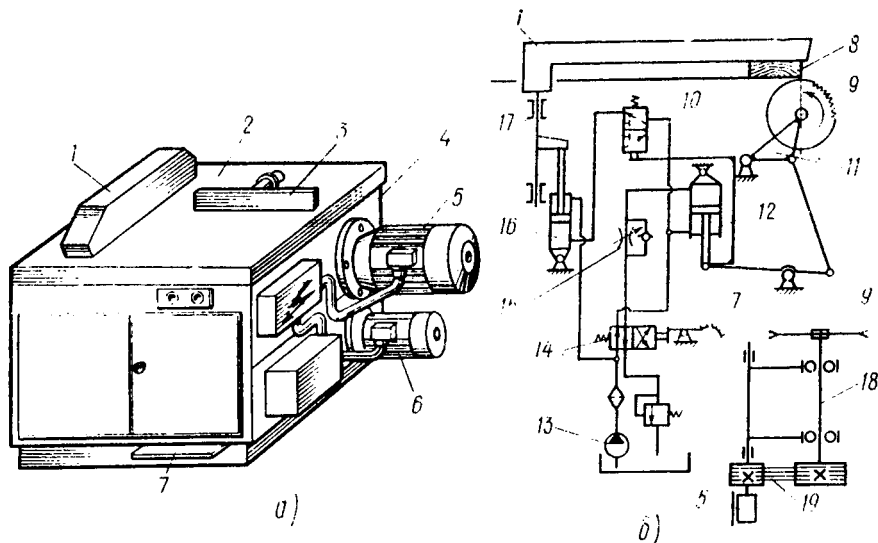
Балансирный торцовочный станок ЦКБ40-01:
